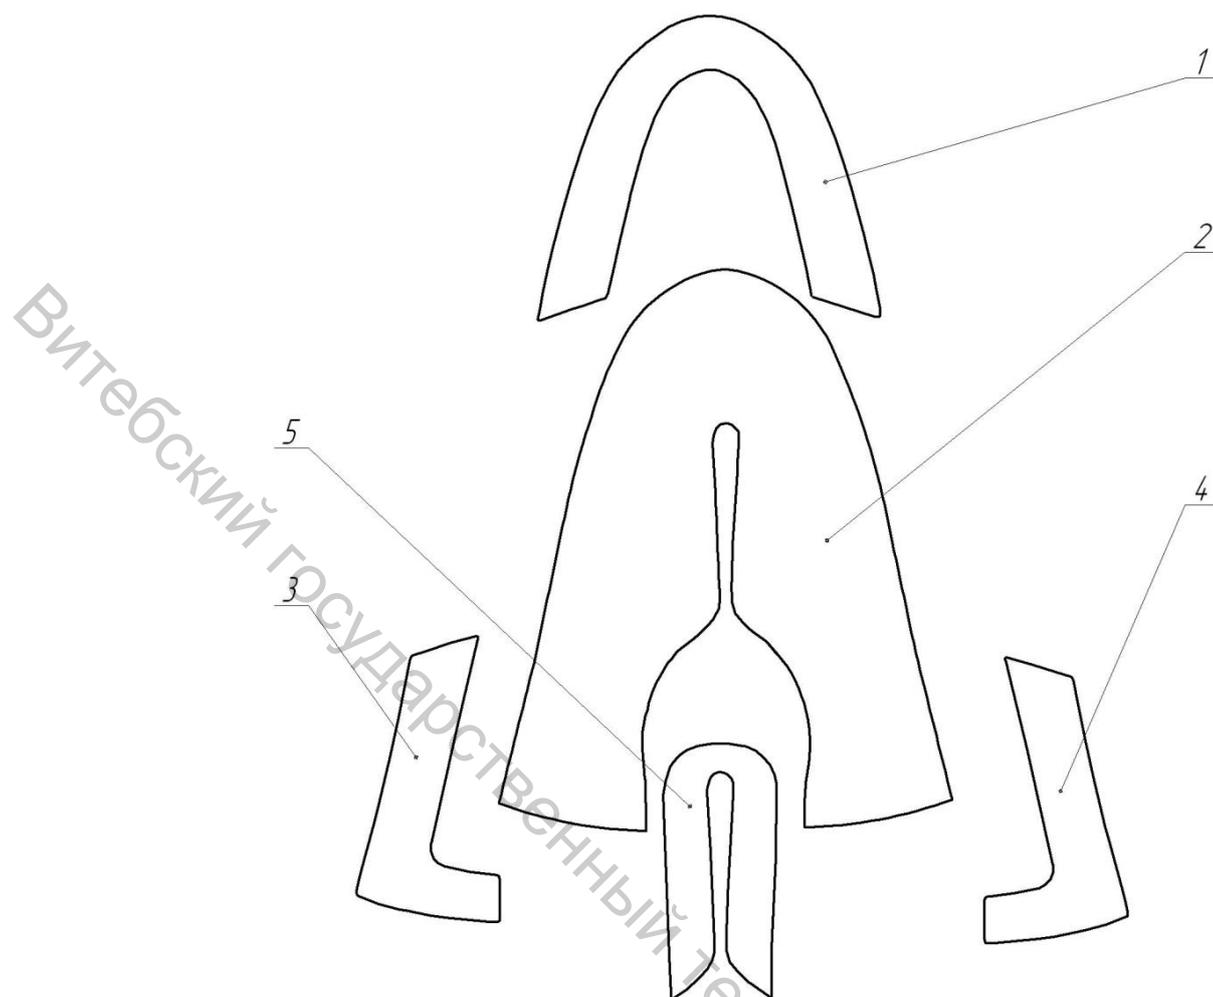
Комплектующие детали плоской заготовки:
